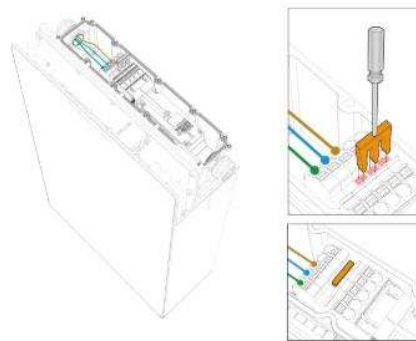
Conexión del cableado de potencia en batería y colocación de puente
